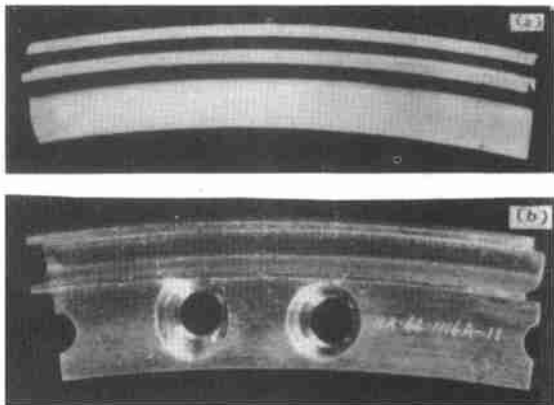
DD4单晶合金封严箍齿环 (a) 毛坯件 (b) 试车件
